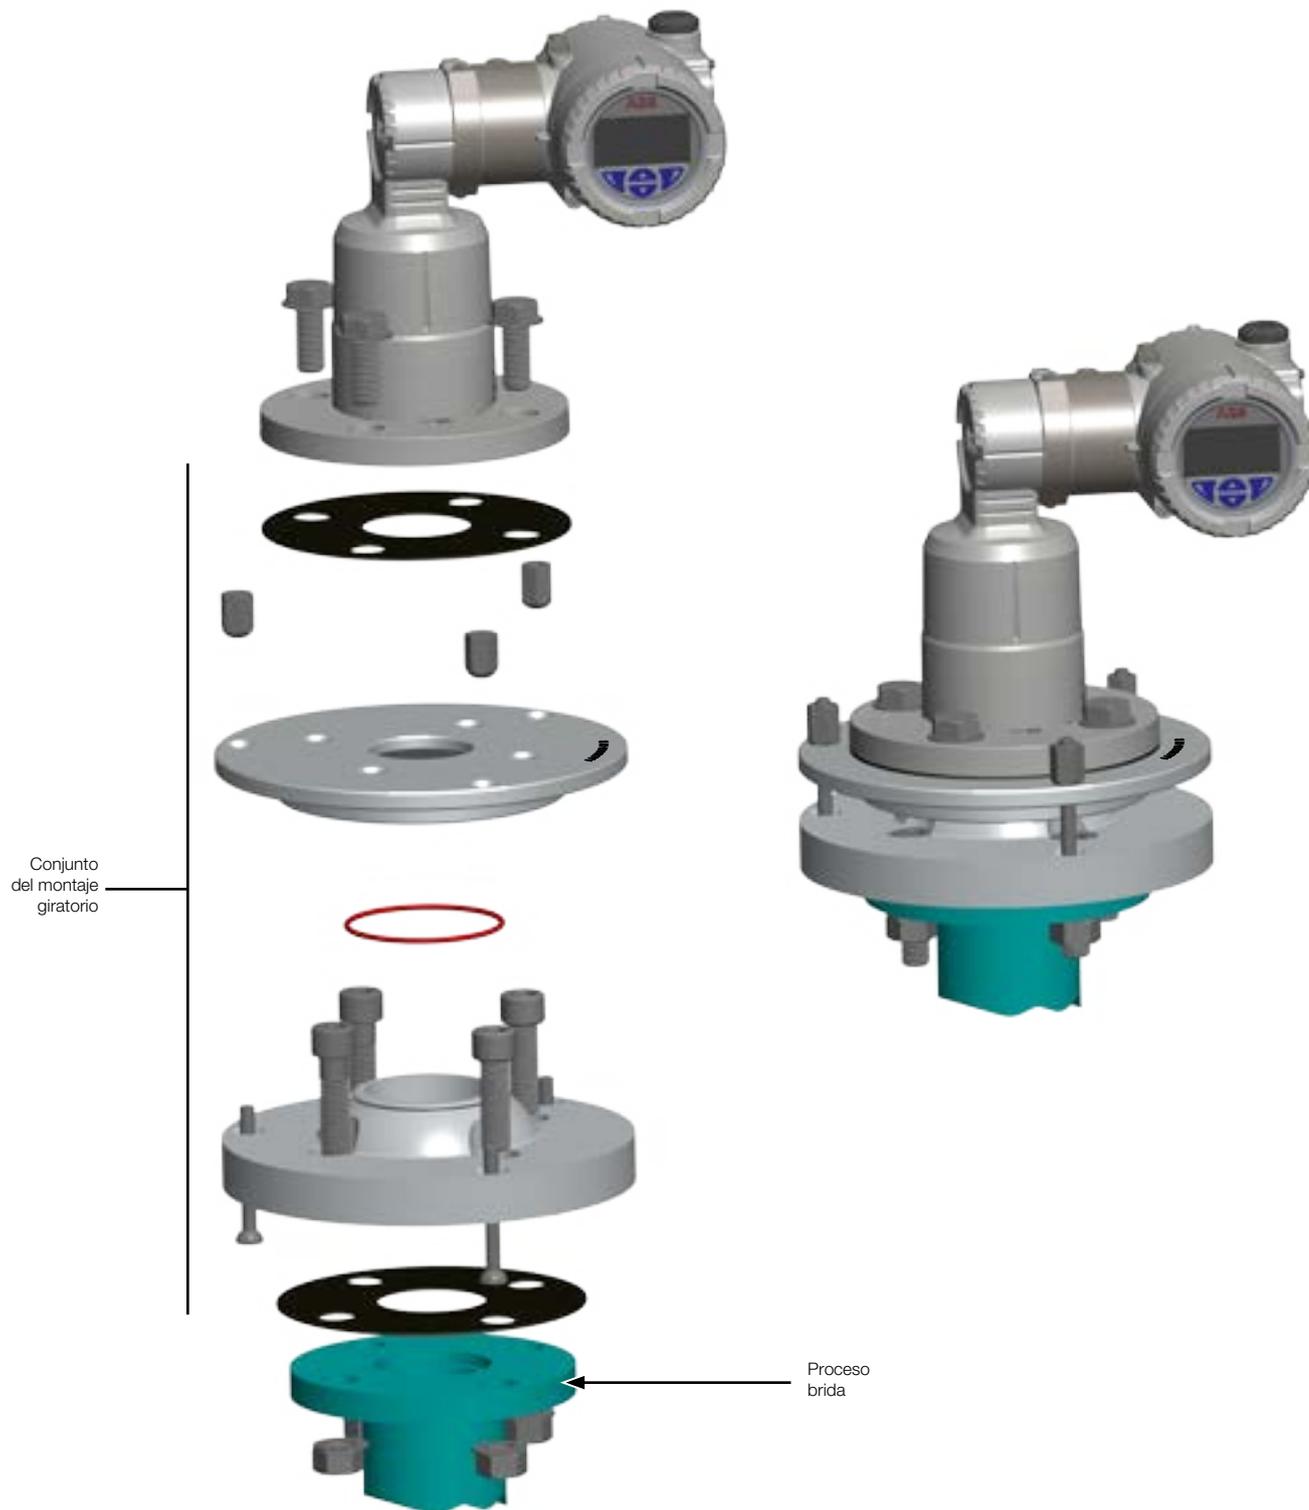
Piezas del montaje giratorio (izquierda) y el conjunto completo (derecha)
